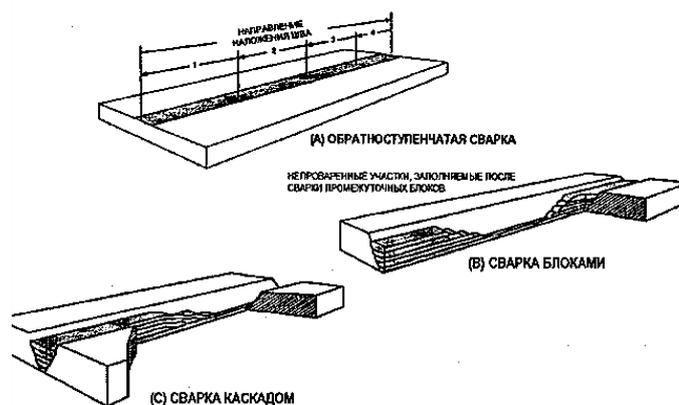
(А-обратноступенчатая сварка, В-сварка Блоками, С-сварка каскадом)
